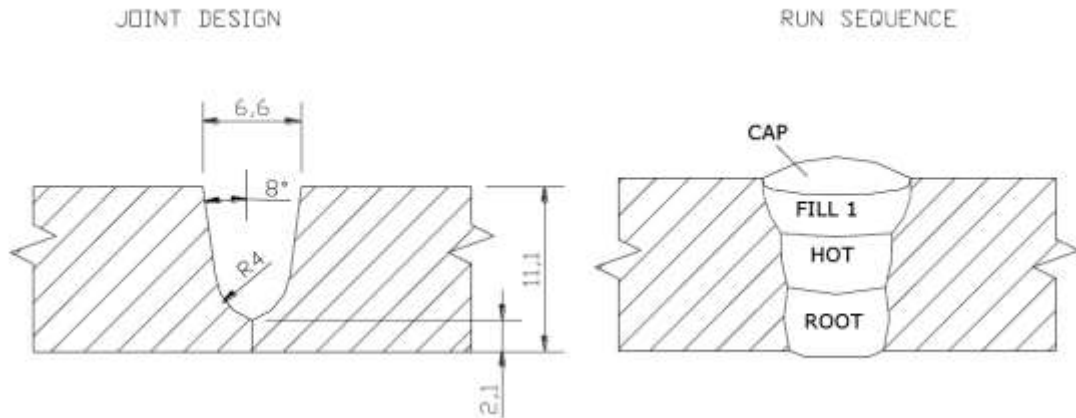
DISEÑO JUNTA Y PASES DE SOLDADURA TECNOLOGÍA CWS 02
